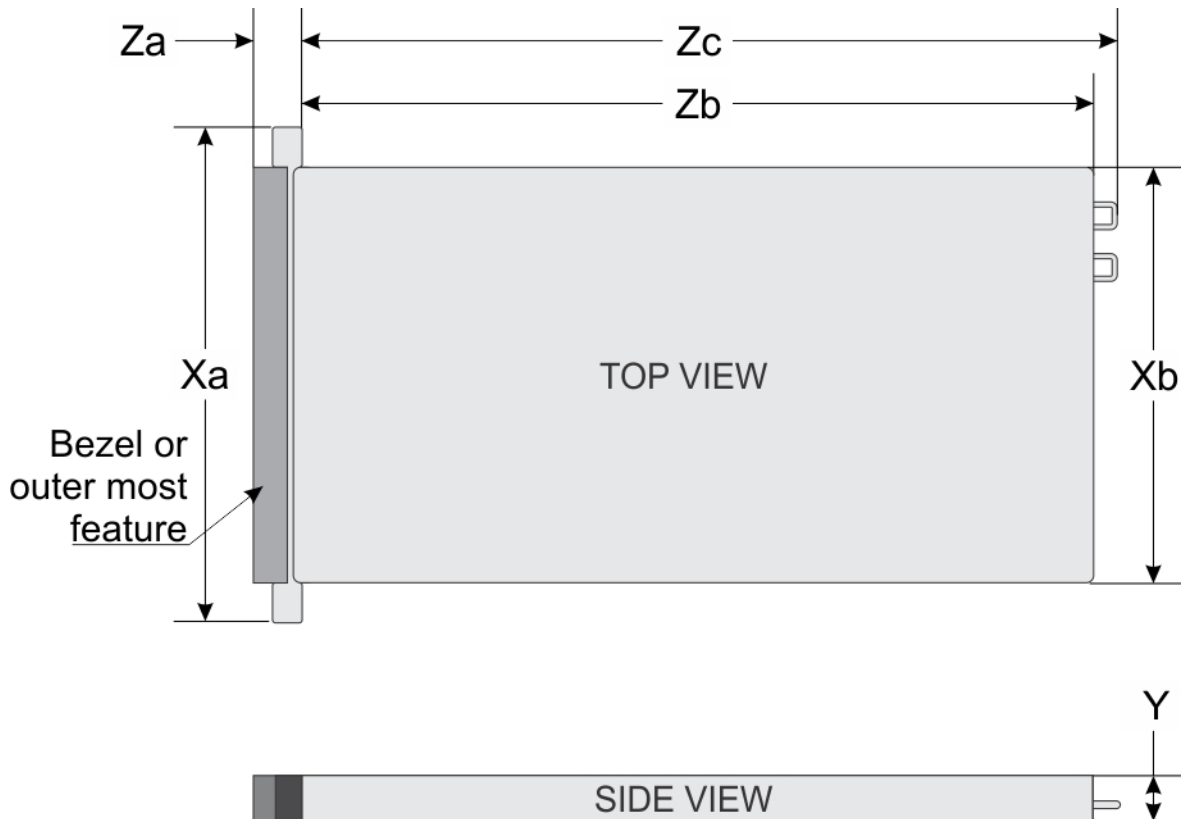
Detalles las dimensiones del sistema Dell PowerEdge C4130
